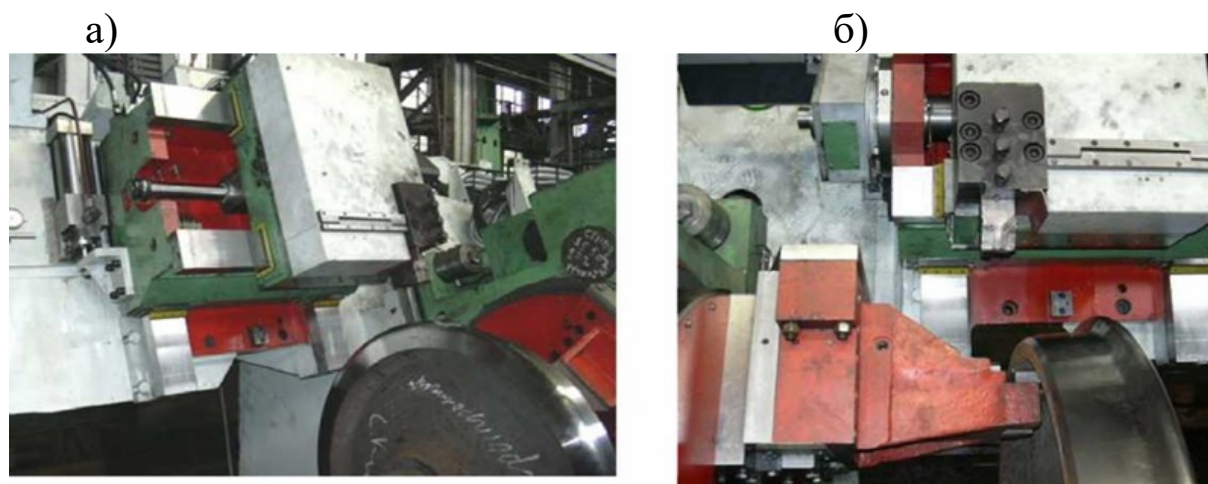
Супорт верстата (а) і гідрокопіювальний повідець привода обертання моделі РТ905Ф3 (б)
